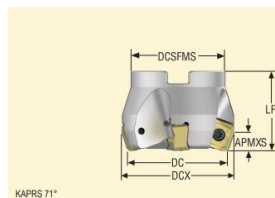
Торцева фреза R220.56-0050-14-4A [7, с.653]
